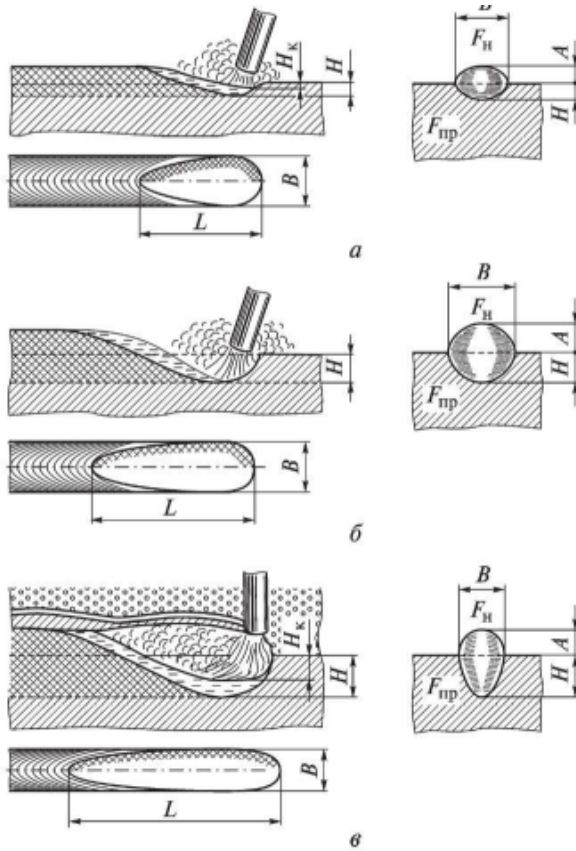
Формы сварочной ванны при дуговой сварке:
